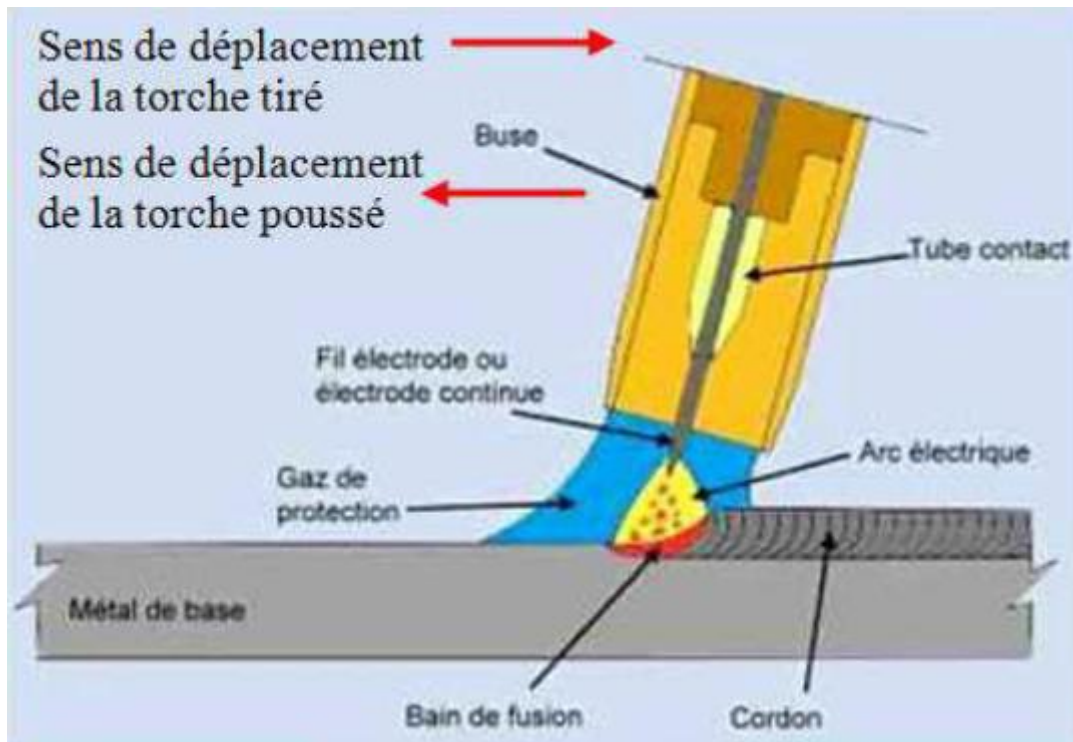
Procédés de soudage MIG/MAG
